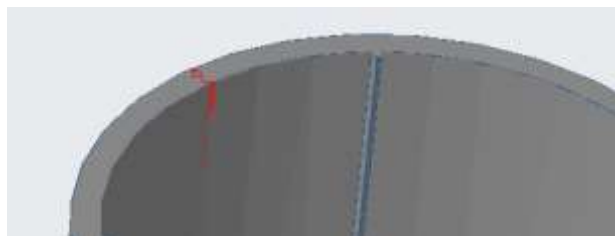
Líneas de soldadura con ataque cortina.
